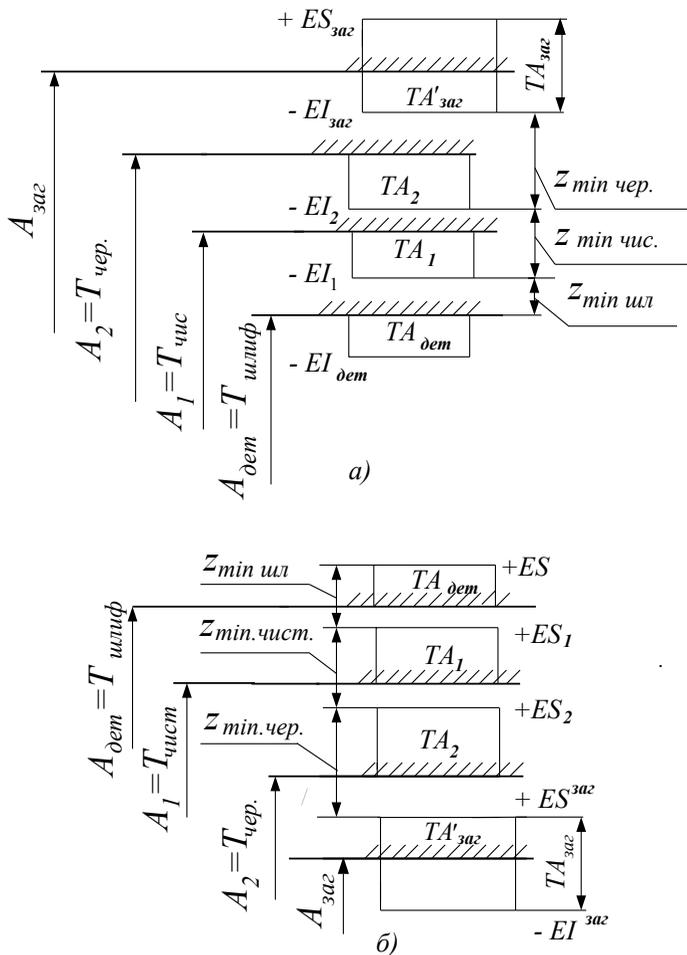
Комбинированные схемы для расчета размера заготовки при обработке на трех технологических переходах: *а* - вала; *б* - отверстия
